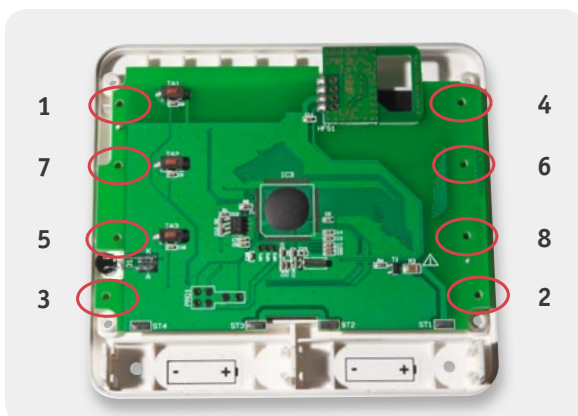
Die Befestigung der Platine erfolgt durch Verschrauben mit 8 Schrauben in der hier vorgegebenen Reihenfolge.
